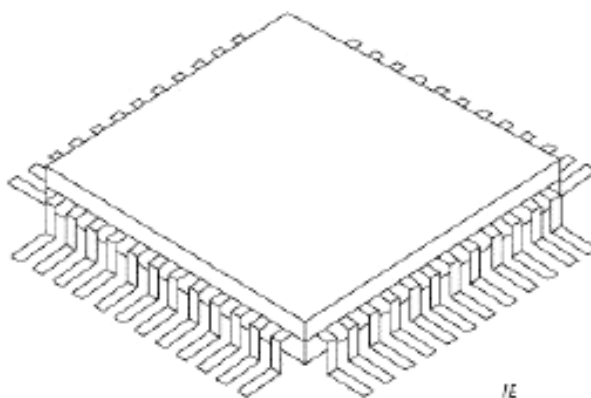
Конструкция корпуса типа PQFP (квадратный)
